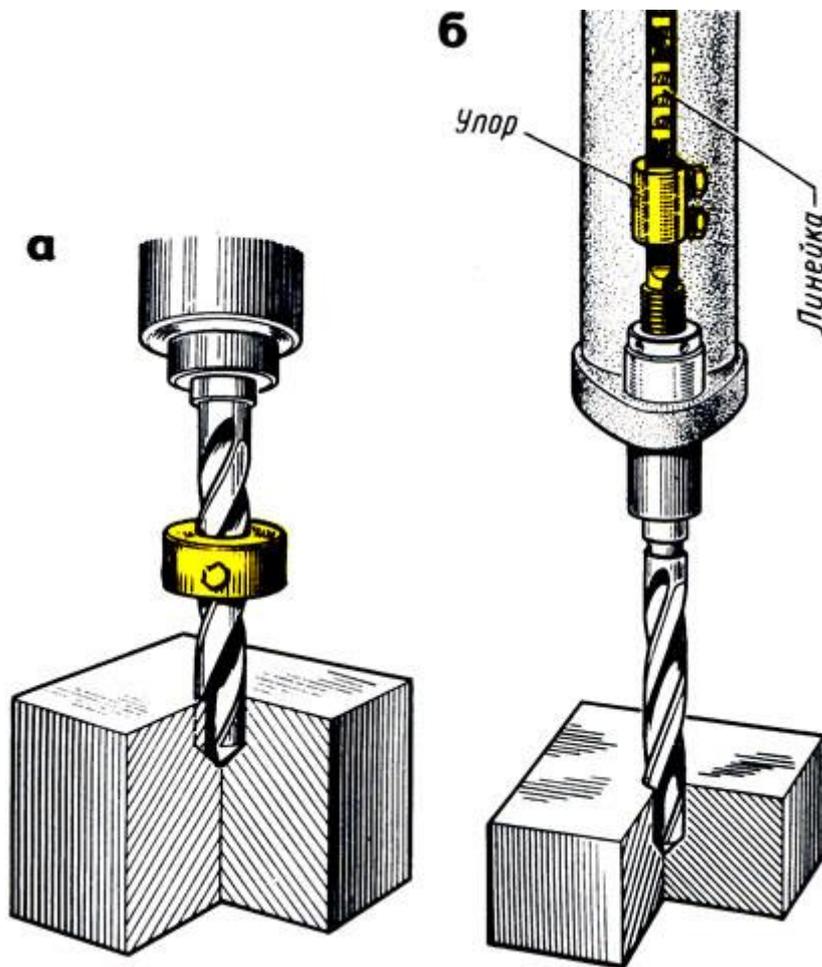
Сверление глухих отверстий на заданную глубину : а - по втулочному упору, Упор б - по измерительной линейке
